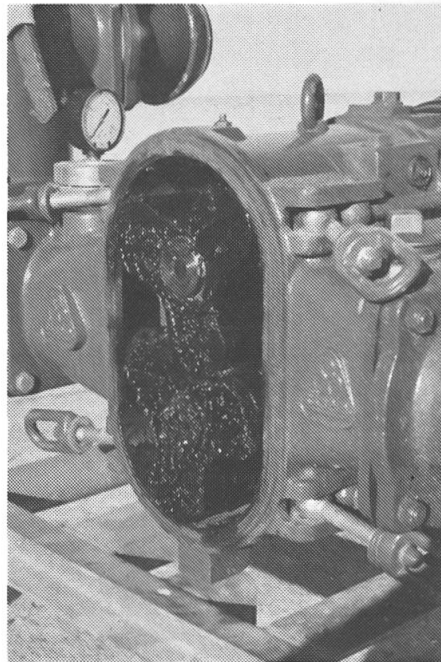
Detailansicht einer Drehkolbenpumpe mit Zugang für Reparaturen im Pumpraum.
